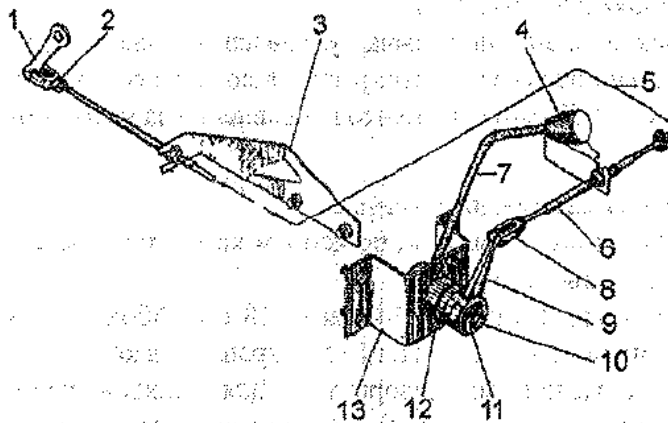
Механизм управления подачей топлива для комбайнов с двигателями СМД: 1 - рычаг топливного насоса; 2, 8 - вилки; 3 - кронштейн; 4 - головка; 5 - стопорный винт; 6 - рукоятка привода подачи топлива; 7 - тросе двустороннего действия; 9 - рычаг; 10 - пружина; 11 - болт регулировочный; 12 - шайбы фрикционные; 13 - кронштейн
